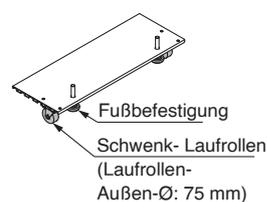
Laufrollen und einstellbare Fußbefestigung (2 Stk.)
